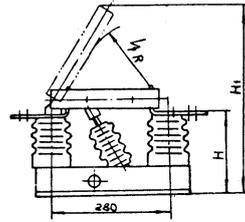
Разъединитель однополюсный типоразмера РЛВОМ 10-11/1000 I УХЛ2, Т2
